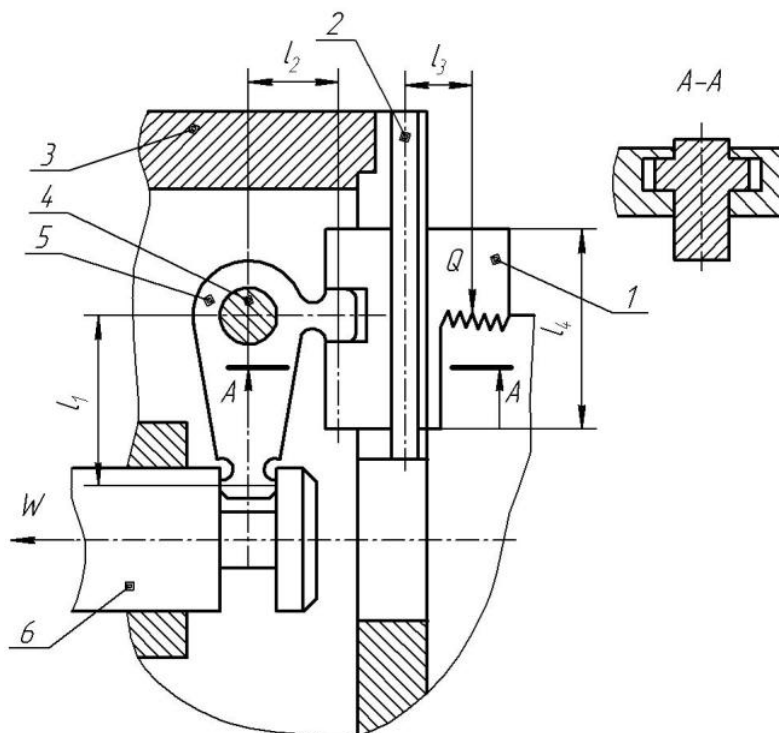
Схема рычажного самоцентрирующего патрона
